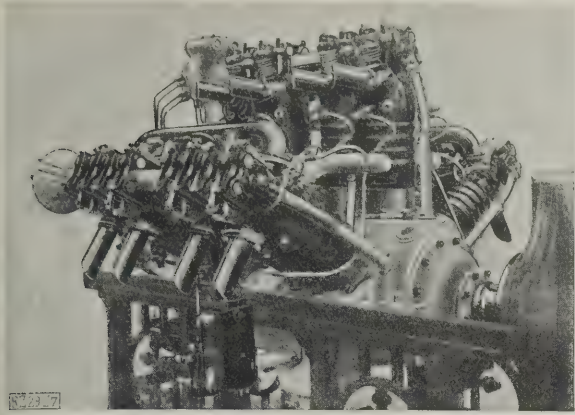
450 PS-Lorraine-Dietrich-Motor mit 3×4 paarweise angeordneten Zylindern und gewellten Stahlblech-Kühlwassermänteln.
